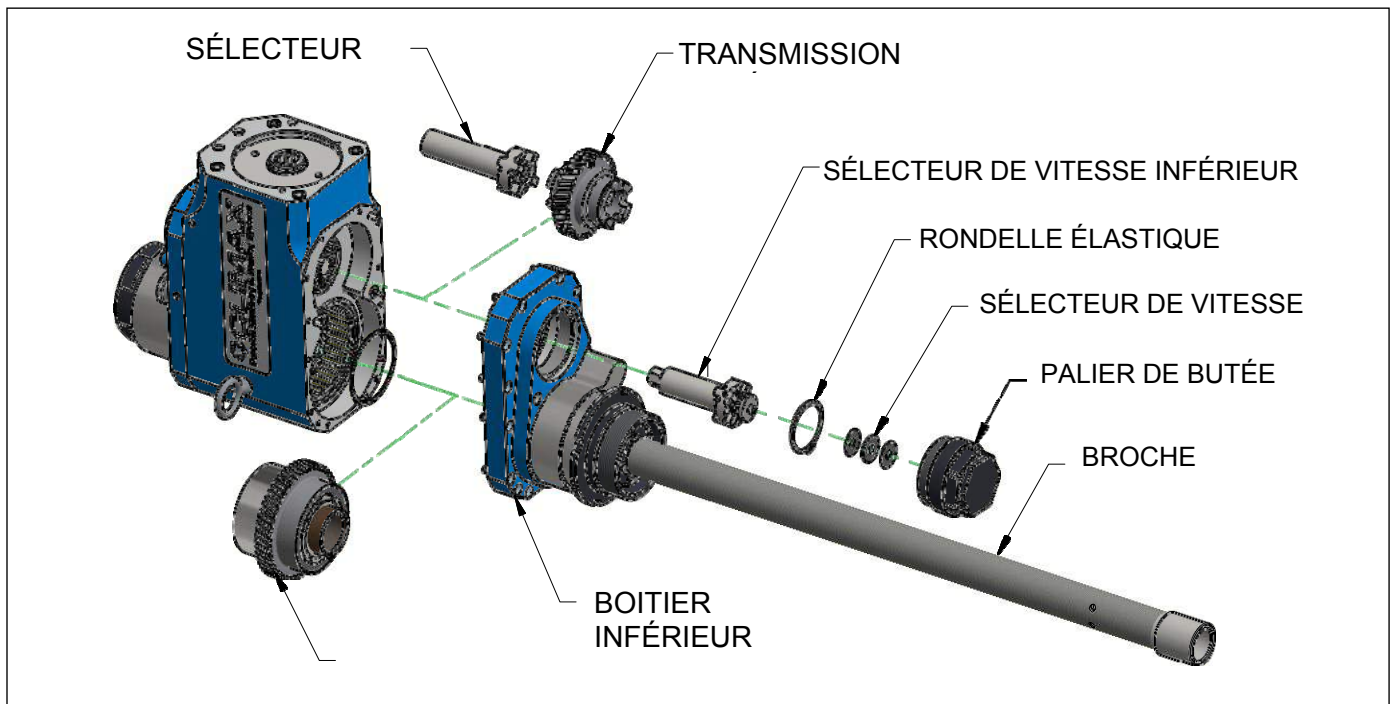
ENSEMBLE DE TRANSMISSION
